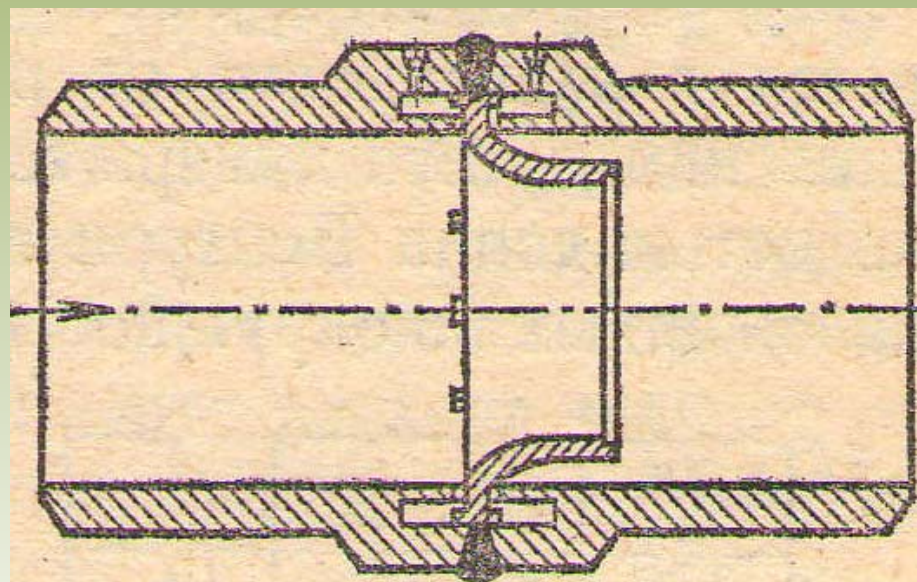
Стандартное сопло с кольцевыми камерами в патрубках со сварным соединением ($m > 0,444$).
